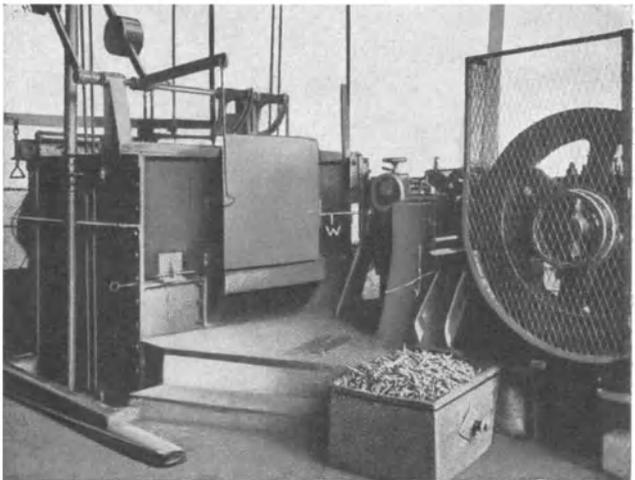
u. 64. Halbwarmpresse und Ofen mit Zuführungsgetriebe
